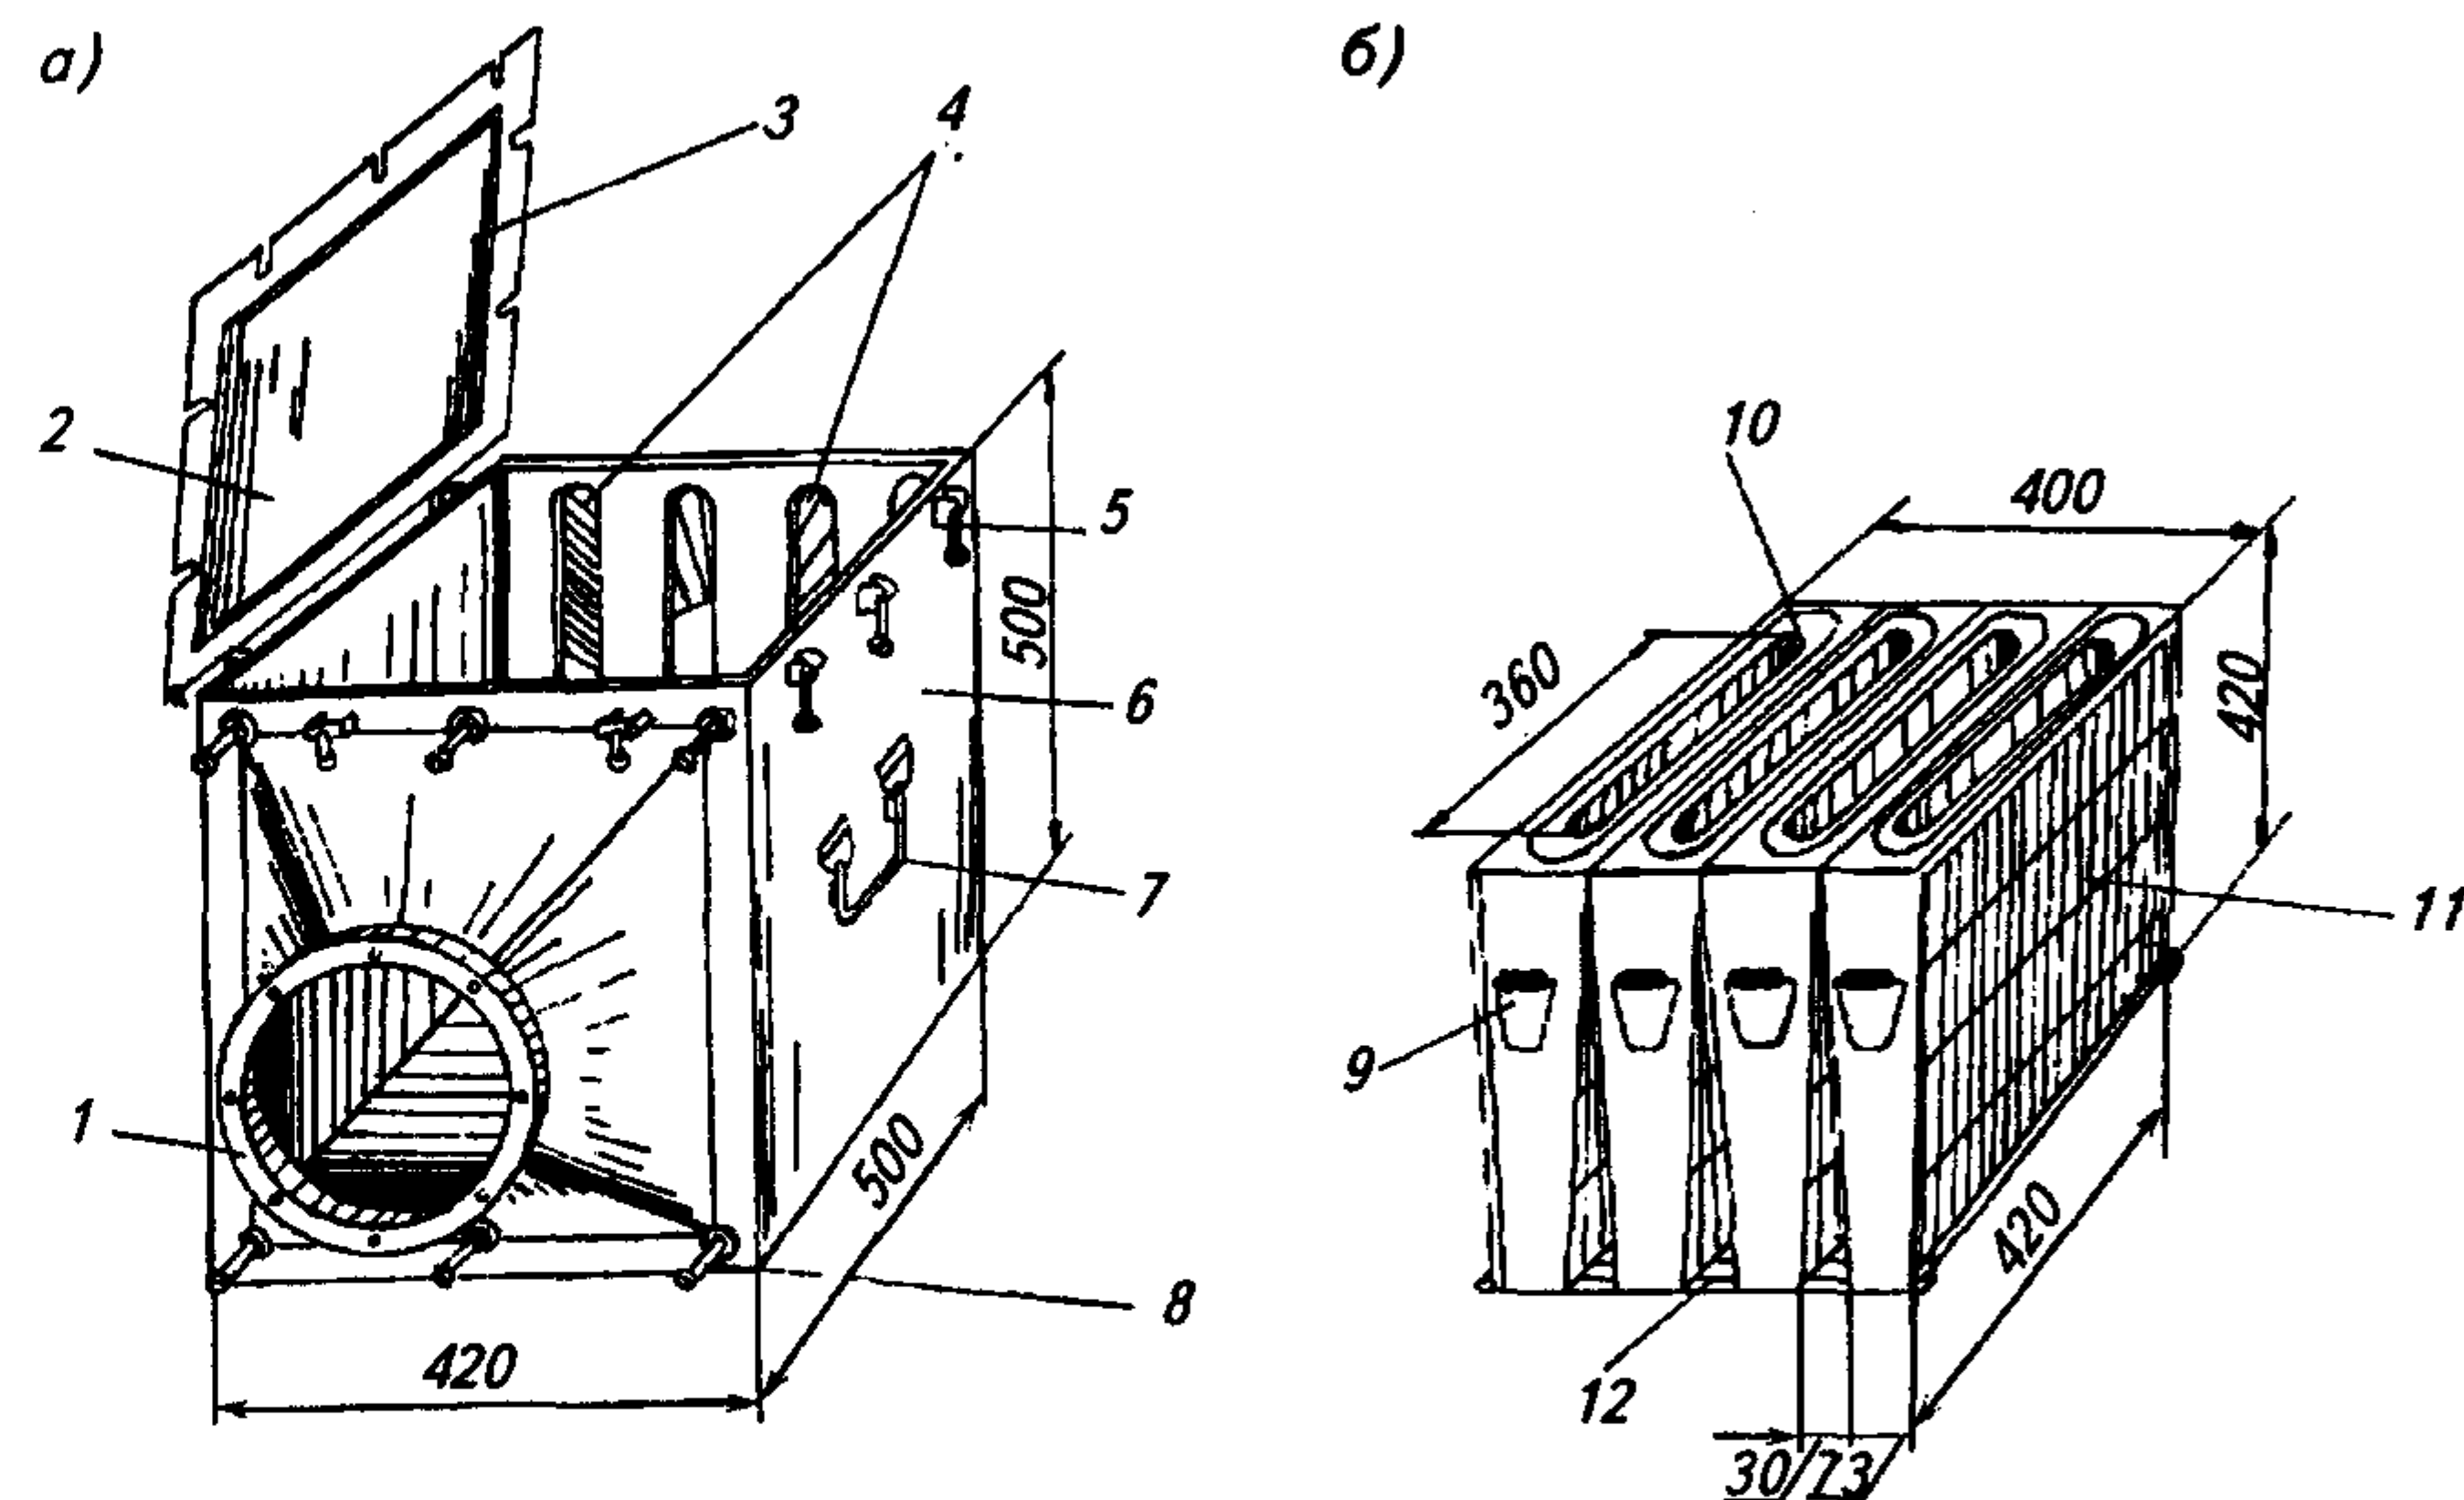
Пакетный противопыльный фильтр: а — корпус; б — фильтрующий пакет; 1 — выходной патрубок; 2 — крышка корпуса; 3 — уплотнение крышки; 4 — входные отверстия в фильтрующую кассету; 5 — откидные болты; 6 — корпус; 7 — ручка; 8 — поджимные болты; 9 — ручка; 10 — кольцевой выступ для герметизации входных отверстий кассет; 11 — фильтрующий картон; 12 — крепление кассет
